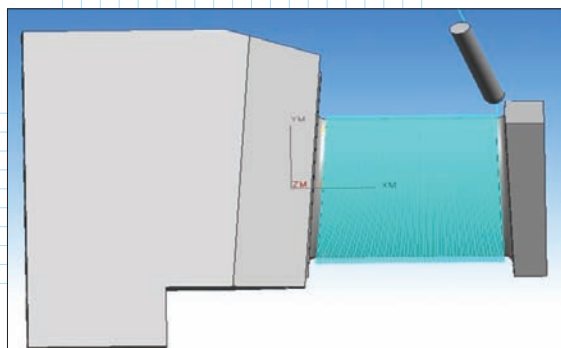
Чистовое фрезерование двуполочной лопатки сферическим инструментом со сложным управлением оси инструмента
